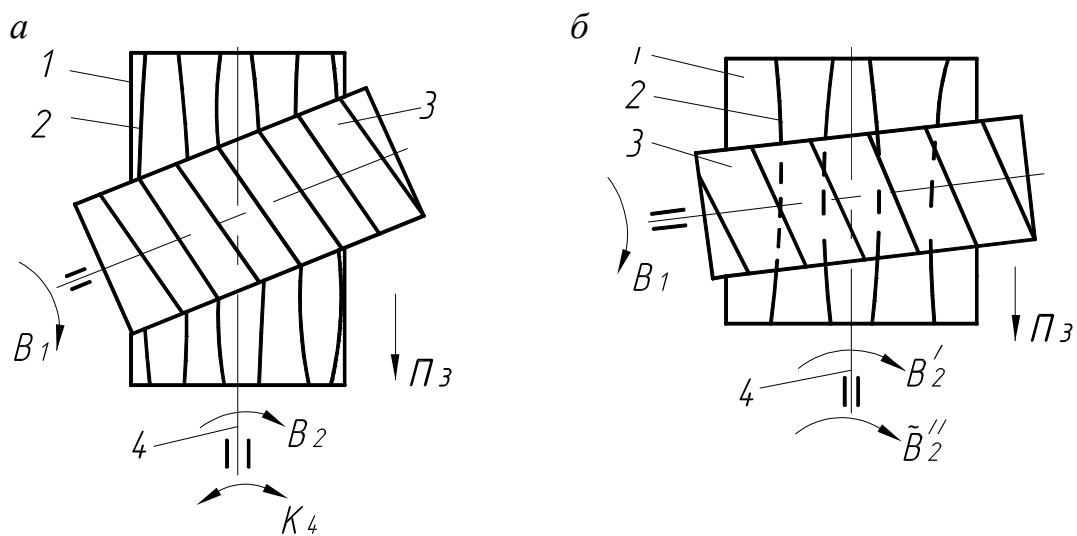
Схемы обработки бочкообразных зубьев при совмещении движений:
